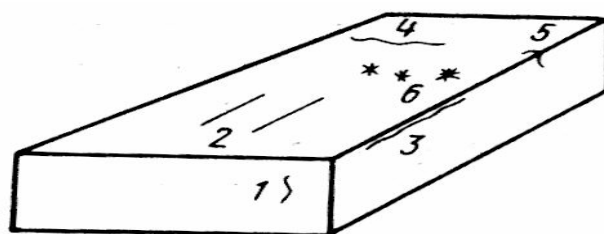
Види тріщин на поверхні безперервнолитої заготовки
